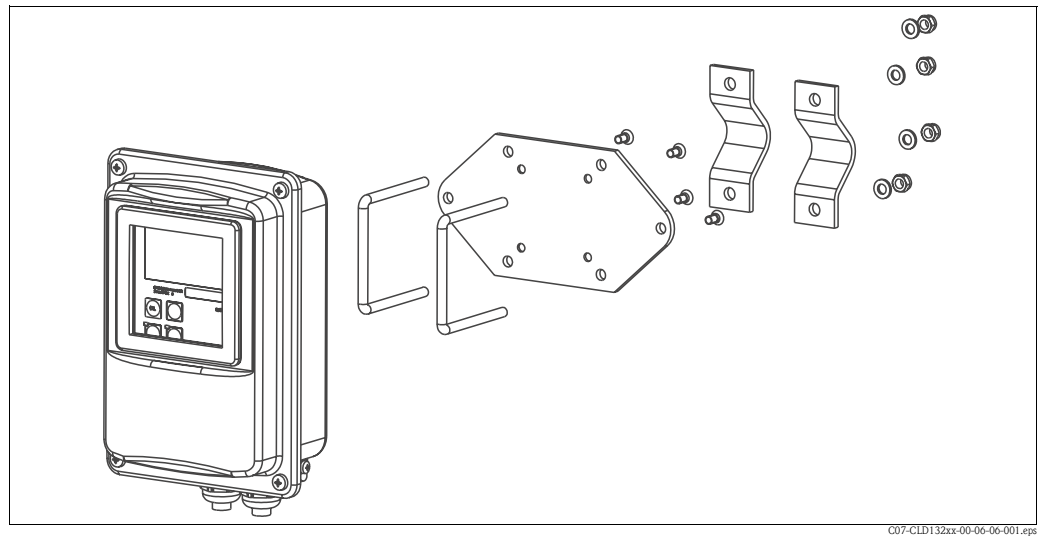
Kit de montage sur mât pour CLD132 version séparée
